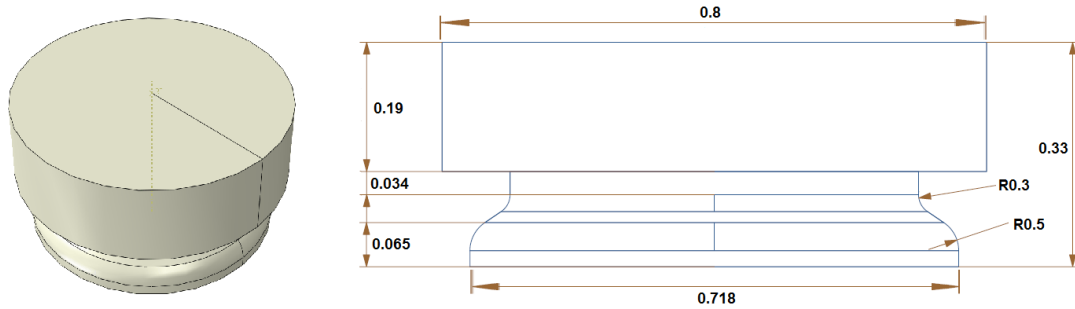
Geometría del rodillo 1, dimensiones en [m].
